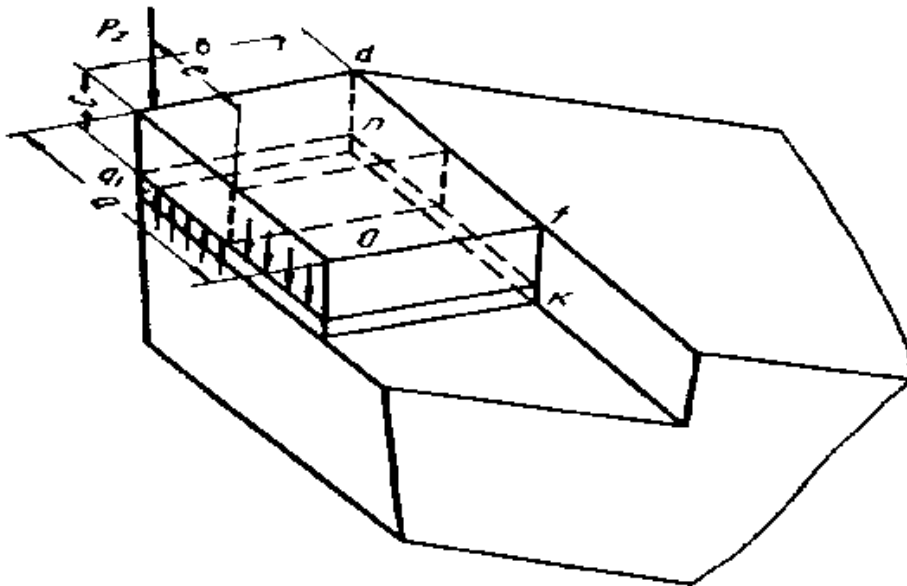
Расчетная схема режущей части токарного резца для определения напряжений [112]
